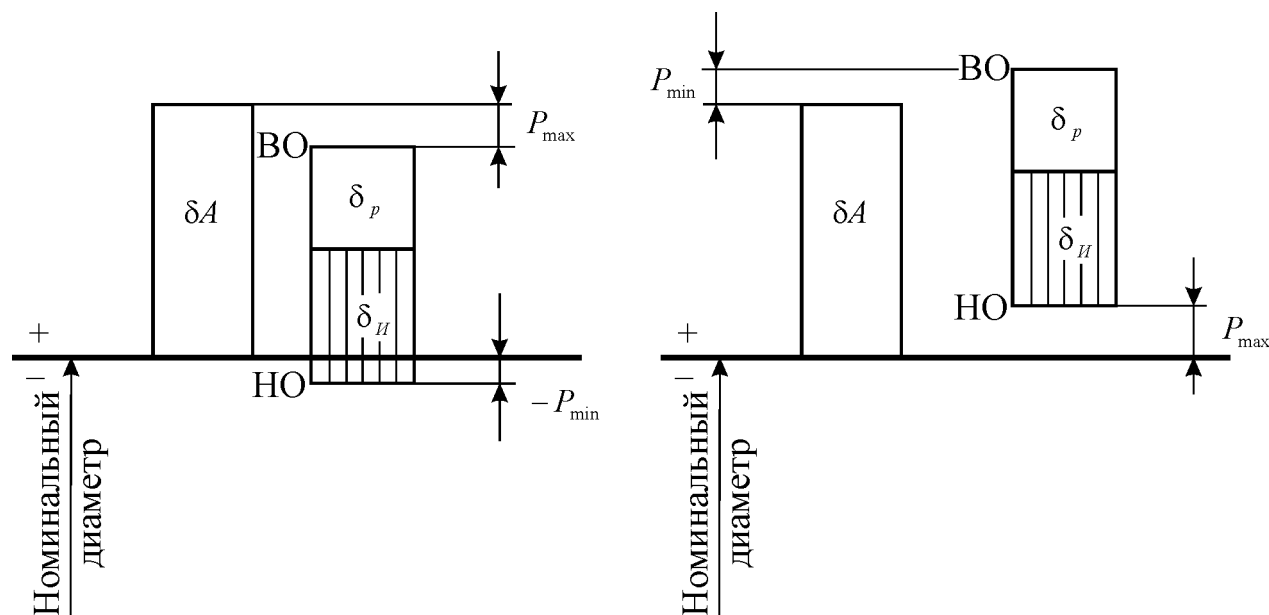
Схемы расположения полей допусков на диаметр развертки и отверстия: а – при положительной разбивке отверстия; б – при отрицательной разбивке отверстия
